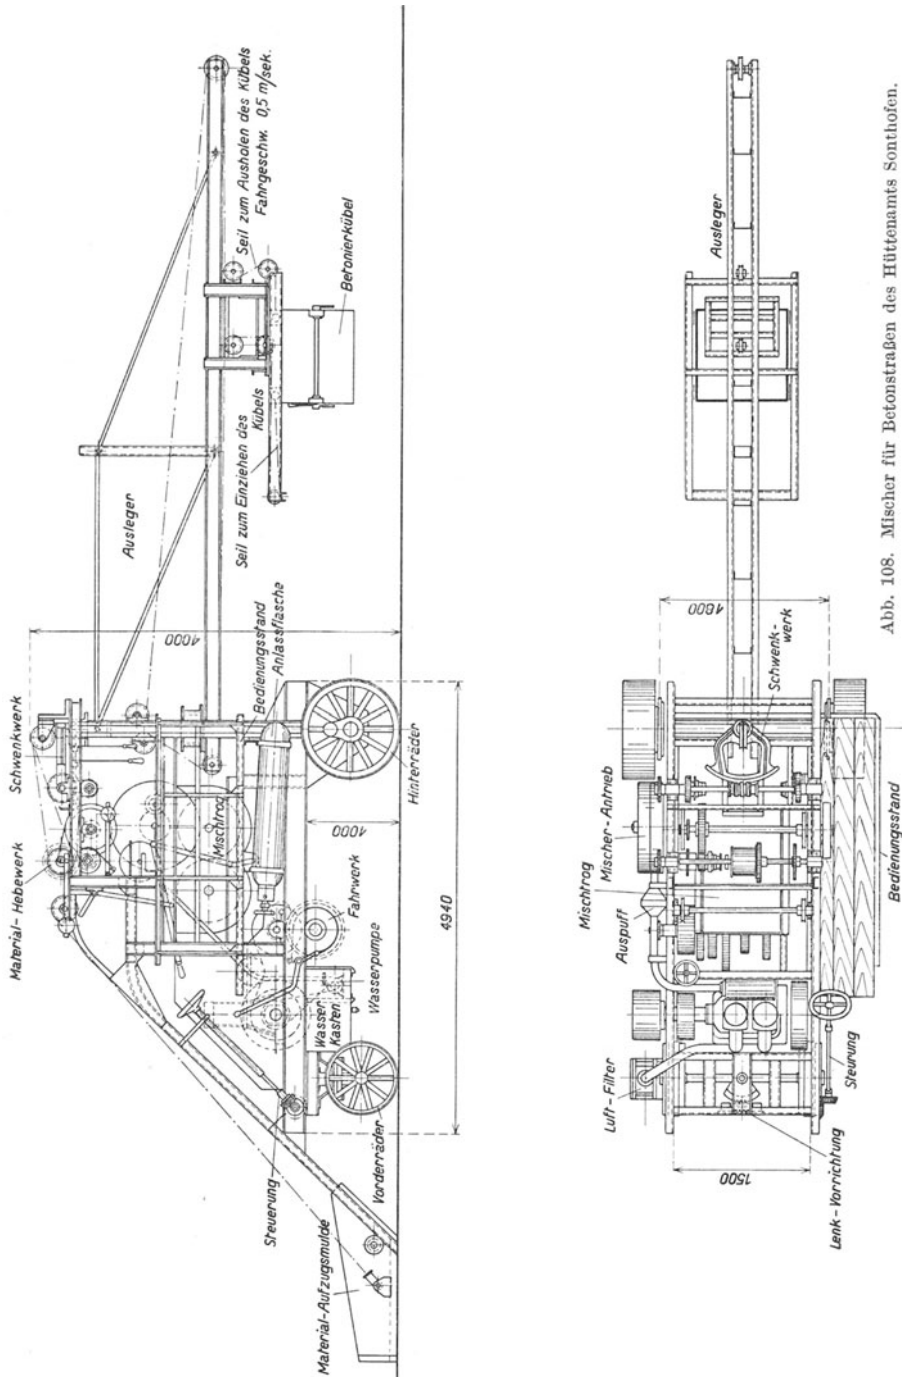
Mischer für Betonstraßen des Hüttenamts Sonthofen.
